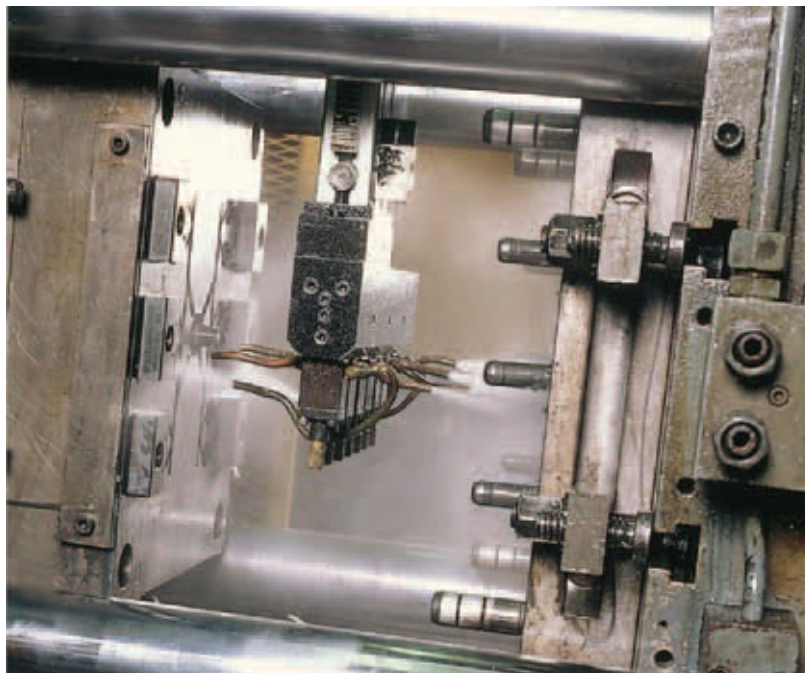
Pulverizador desmoldante automático. [C'-41]
